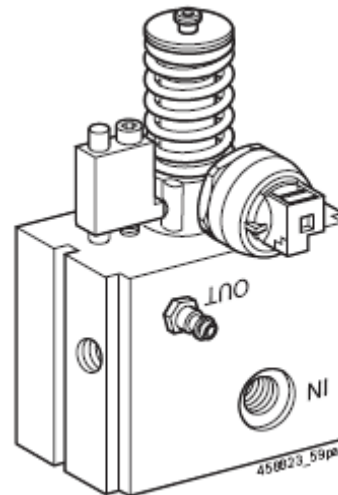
Тестовый адаптер с креплением при помощи прихвата.
